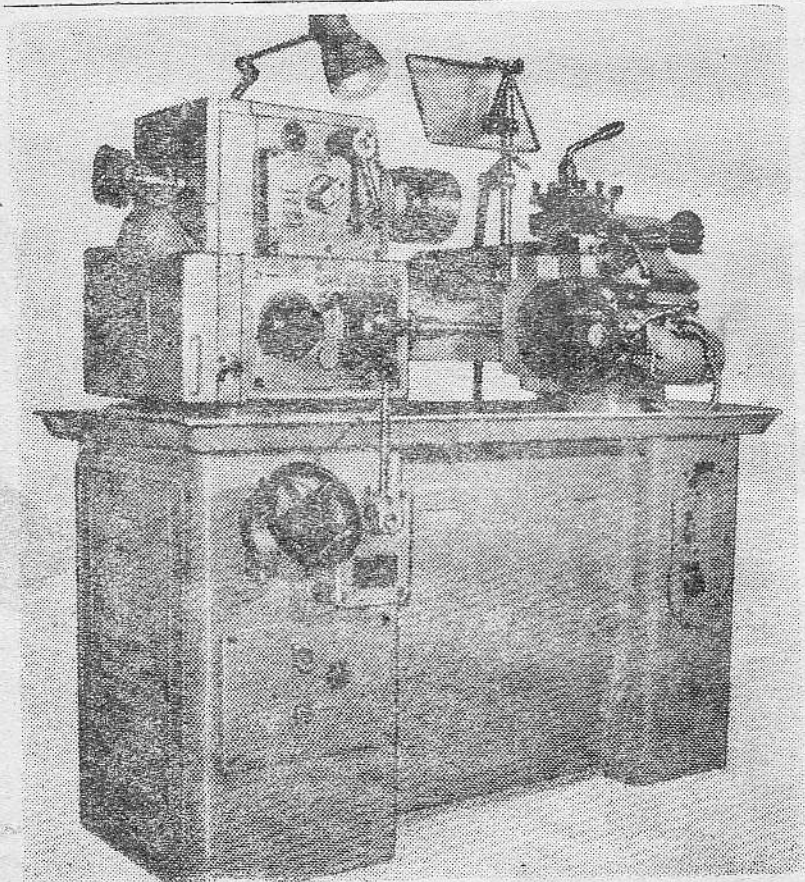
Универсальный токарно-винторезный станок повышенной точности модели 1604
